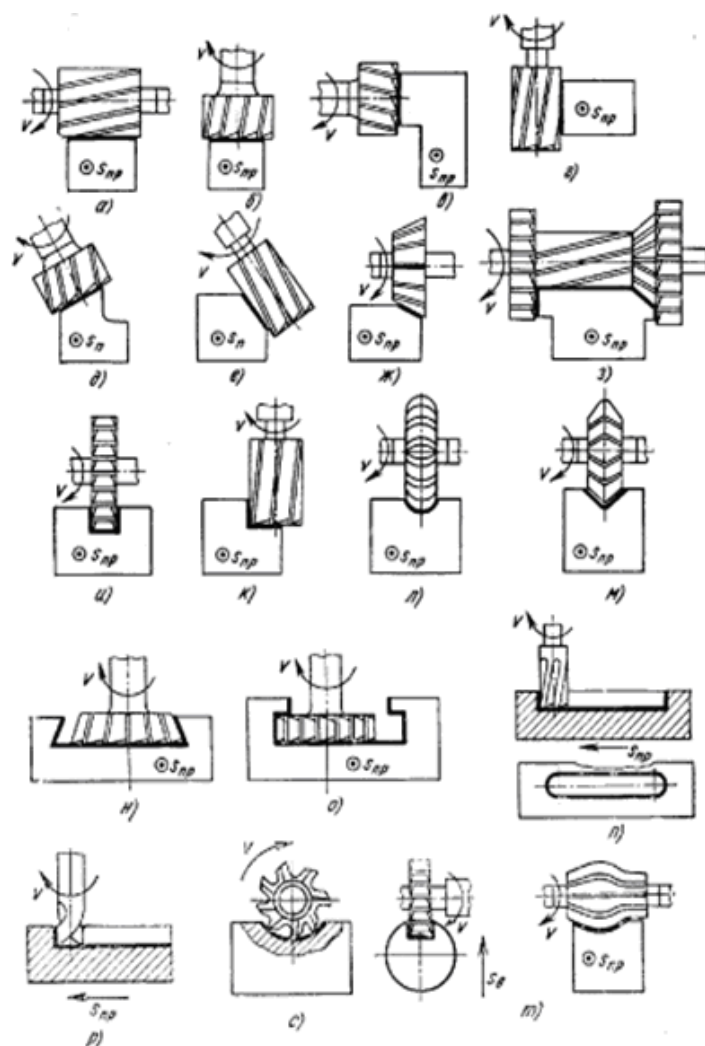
Обработка заготовок на горизонтально- и вертикально-фрезерных станках:
